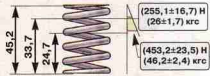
Основные данные для проверки наружной пружины клапана
